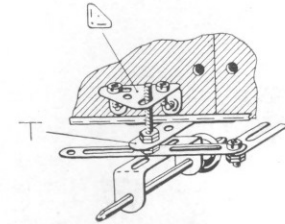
d Befestigung und Lagerung einer Vorderradachse.
